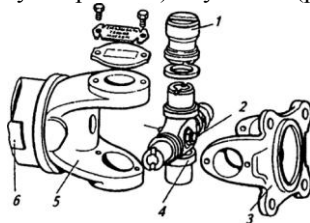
Конструкція карданного шарніра нерівних кутових швидкостей: 1 - підшипник; 2 - масельничка; 3 - фланець з вилкою; 4 - шип хрестовини; 5 - вилка вала; 6 - карданний вал.
